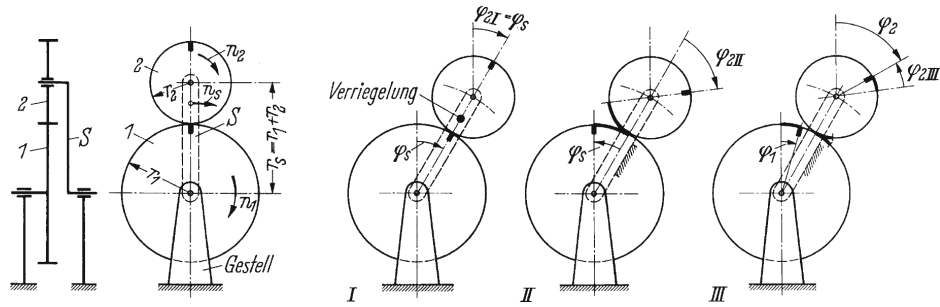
Einfachstes Umlaufgetriebe. [3].
